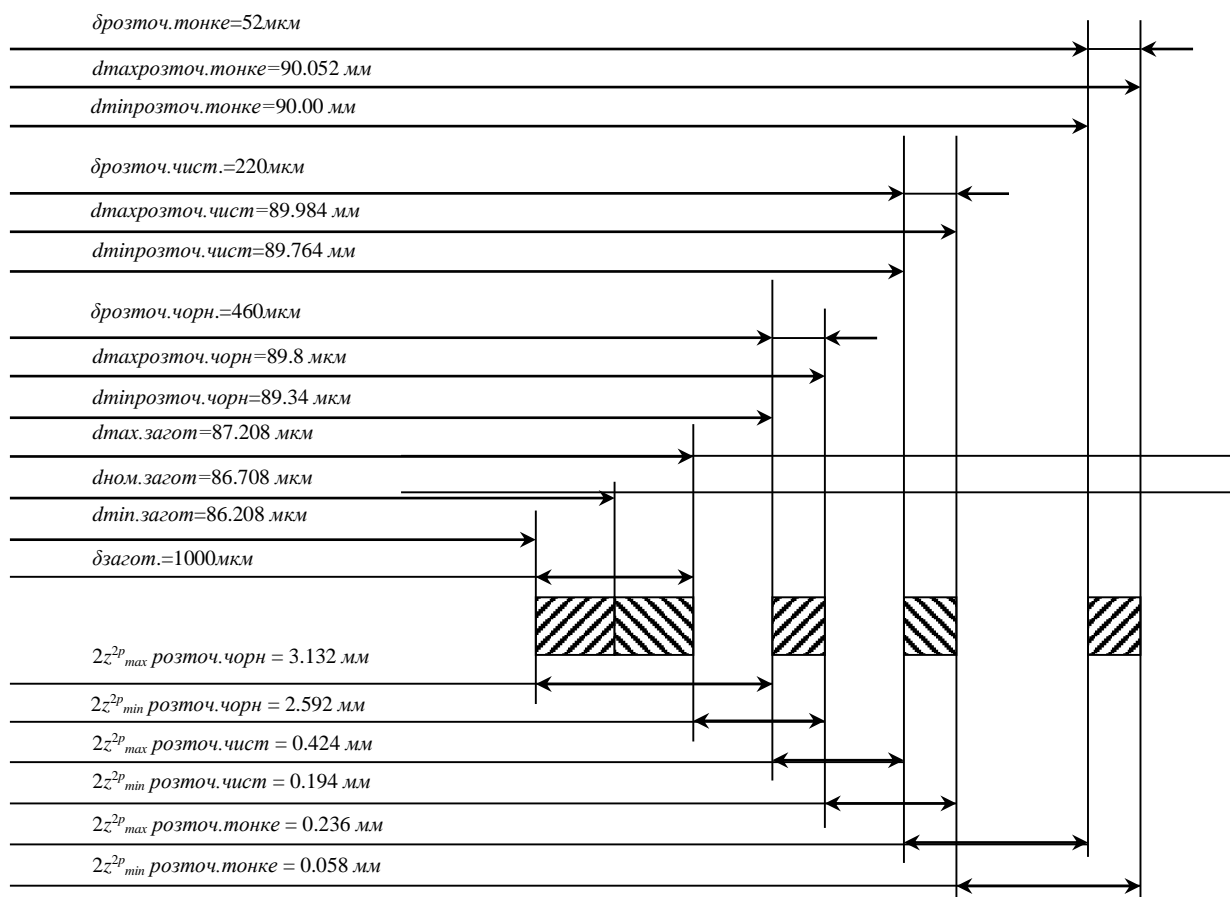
Схема розташування припусків і допусків на обробку розміру
